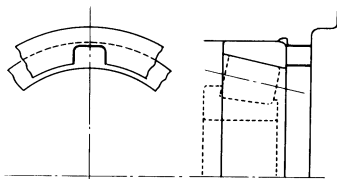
Канавки в корпусе конического роликоподшипника для установки съемника
